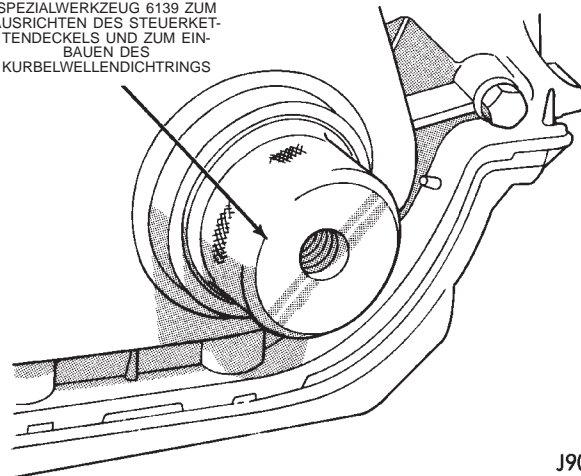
Spezialwerkzeug 6139 zum Ausrichten des Steuerkettendeckels und zum Einbauen des Kurbelwellendichtrings
